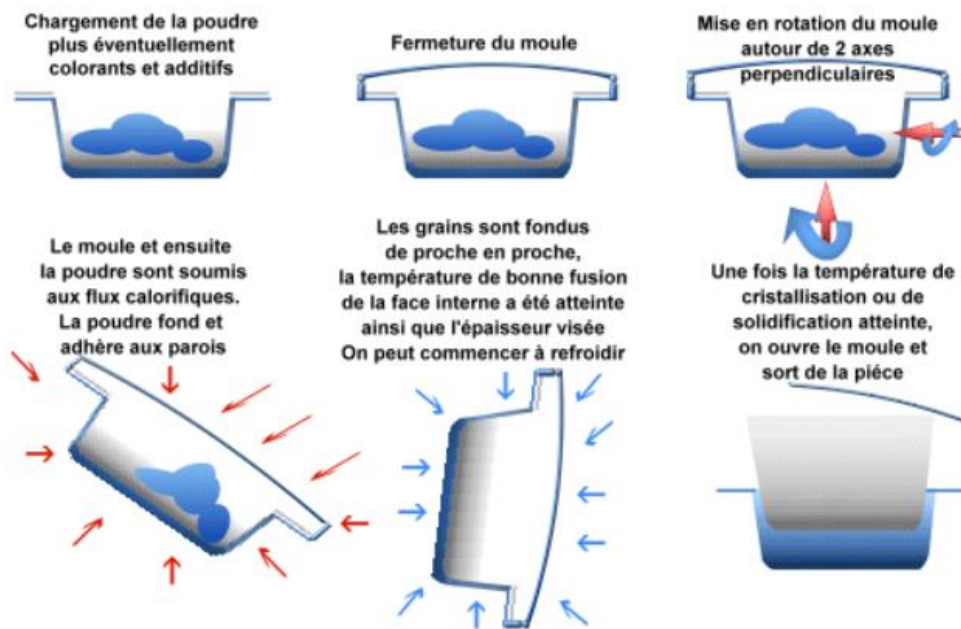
Procédure de roto-moulage, By ROTO-SPEC
